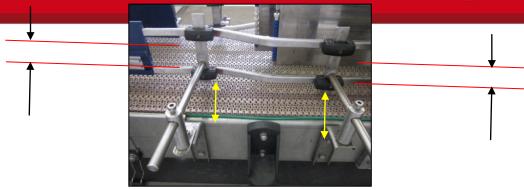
Barandas paralelas dobles Fuente: La Empresa
